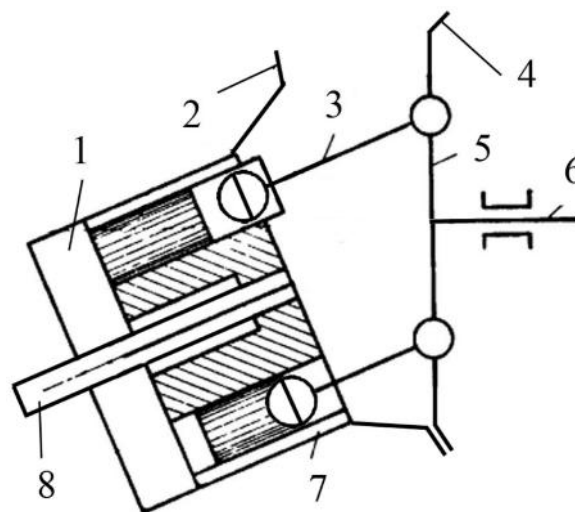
Схема насоса бескарданного типа с зубчатой парой: 1 – распределительная шайба; 2, 4 – зубчатый венец; 3 – шатун-поршень; 5 – упорный диск; 6 – ведущий вал
